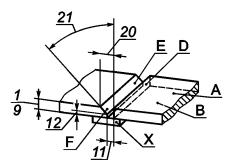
Подготовка под сварку стыкового соединения со скосом одной кромки с притуплением и с подкладкой
